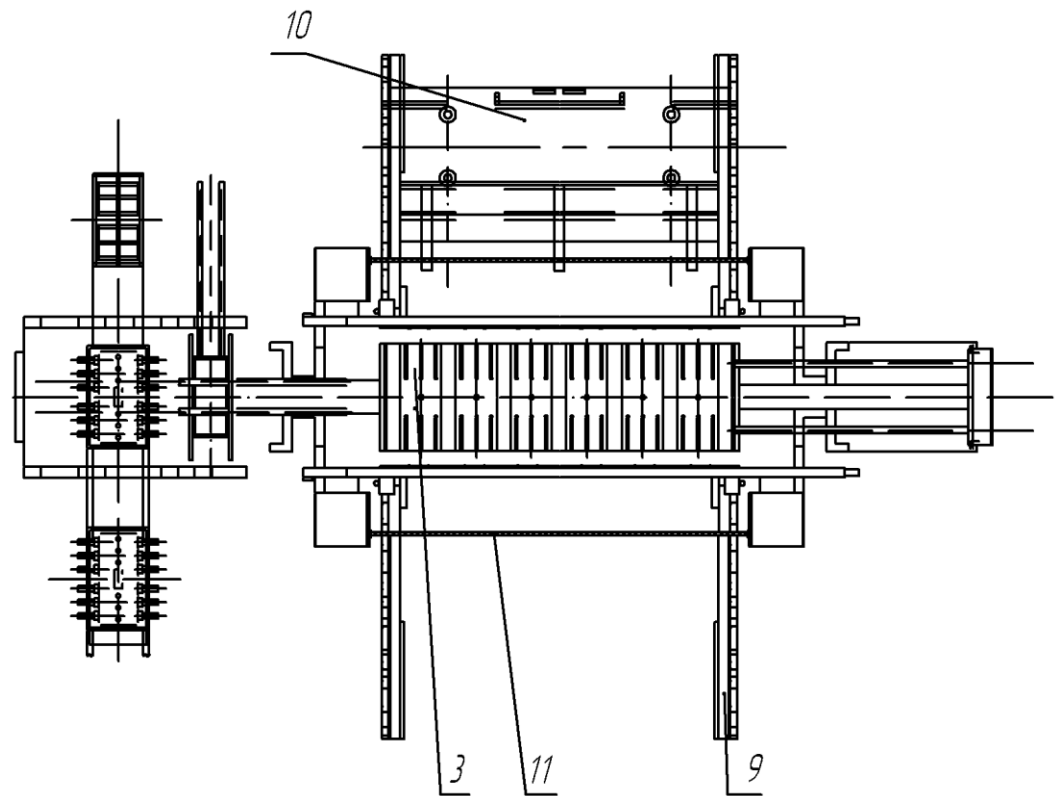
Многопозиционный пресс-автомат Muller Weingarten – 1700 (вид сверху)
